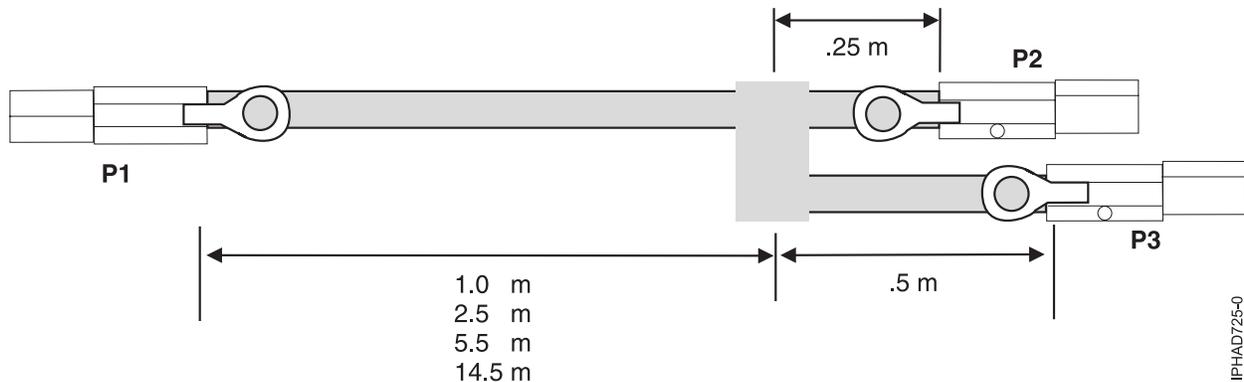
Comprimentos de cabo do conjunto de cabos externos SAS YO
